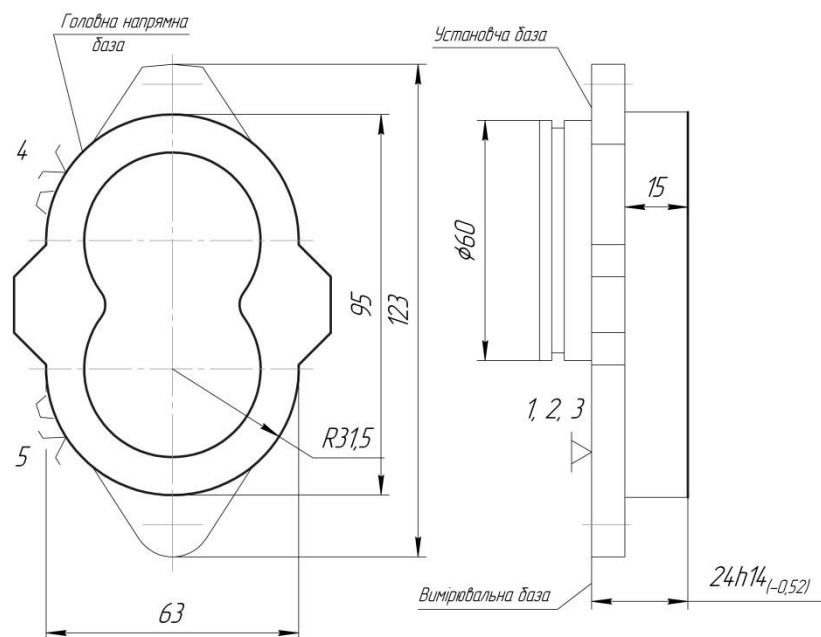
Схема базування заготовки у пристосуванні
